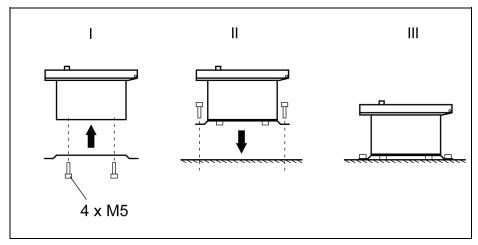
Wandmontage mit Flacheisen (Draufsicht, schematisch)
